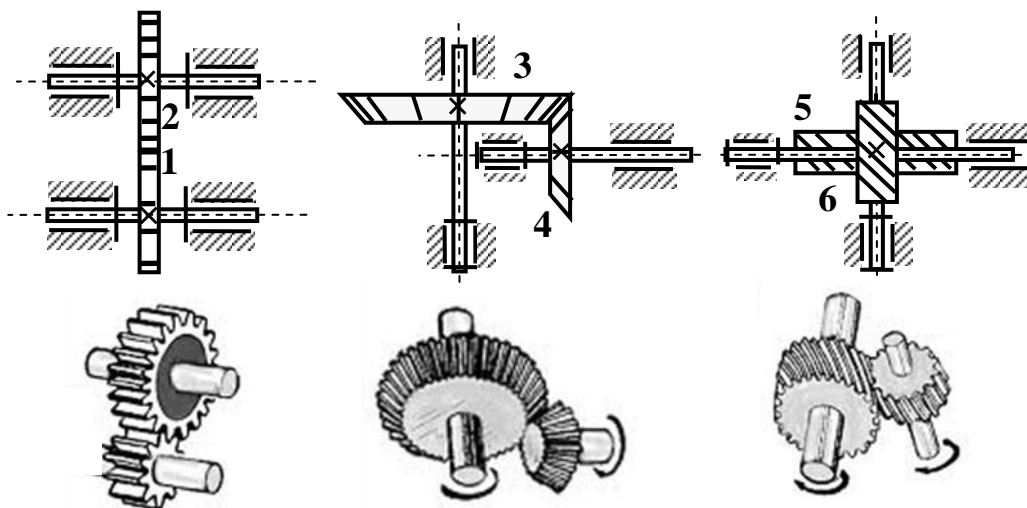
Зубчатый механизм с цилиндрическими колесами 1, 2, коническими колесами 3, 4 и косозубыми колесами 5, 6
